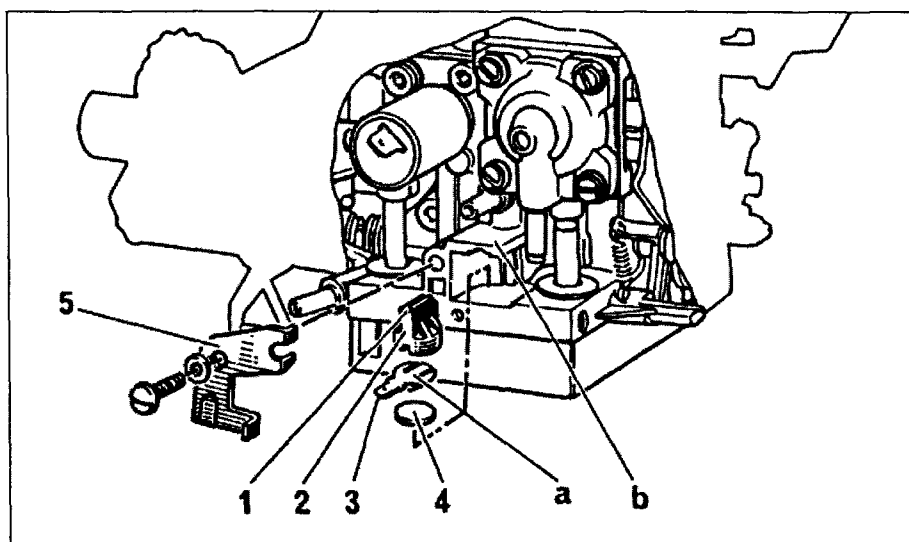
Установка подогревателей корпуса дроссельных заслонок
